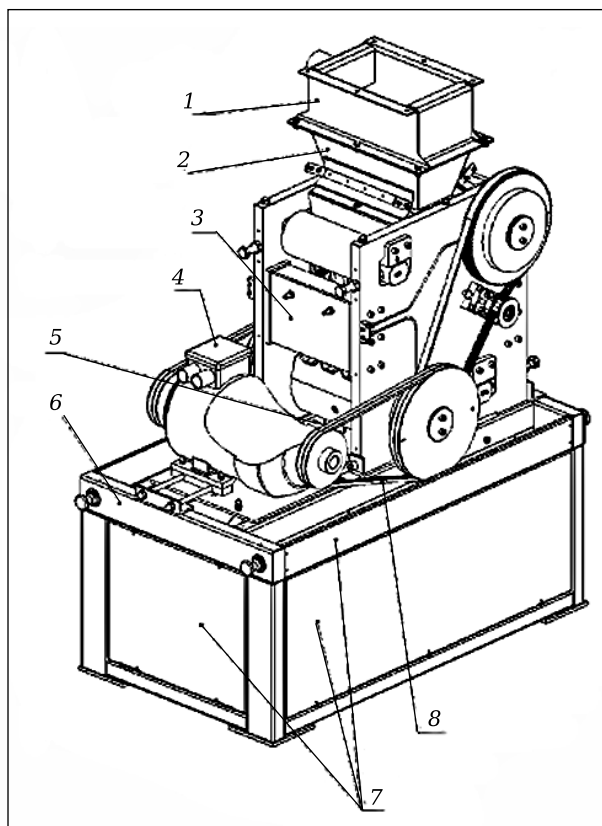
Щековая дробилка ЩДС-I-1,6×3,9 (верхний комплект кожухов условно снят): 1 — бункер; 2 — воронка; 3 — узел дробления; 4 — электродвигатель; 5 — лоток; 6 — рама; 7 — элементы комплекта кожухов; 8 — клиноременная передача
